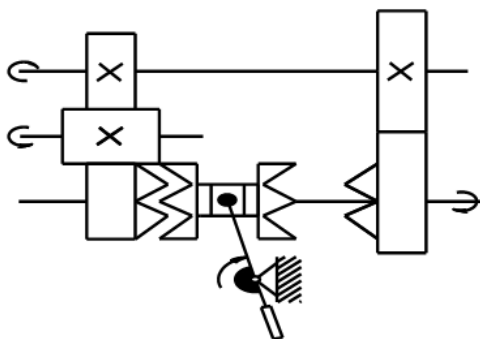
Блок конечного выключателя с автоматическим подключением реверсивного движения обратного хода реечной шестерни (4)
